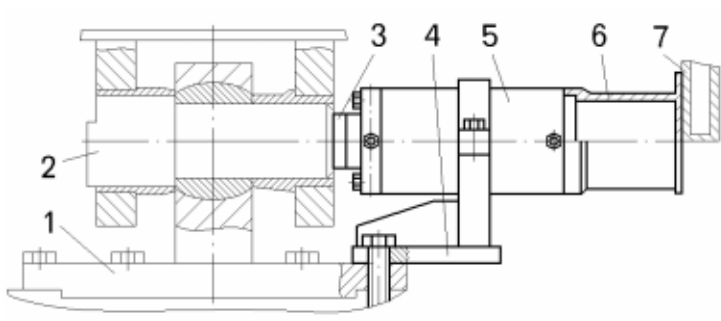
Приспособление для выпрессовки центрального пальца передней подвески:
